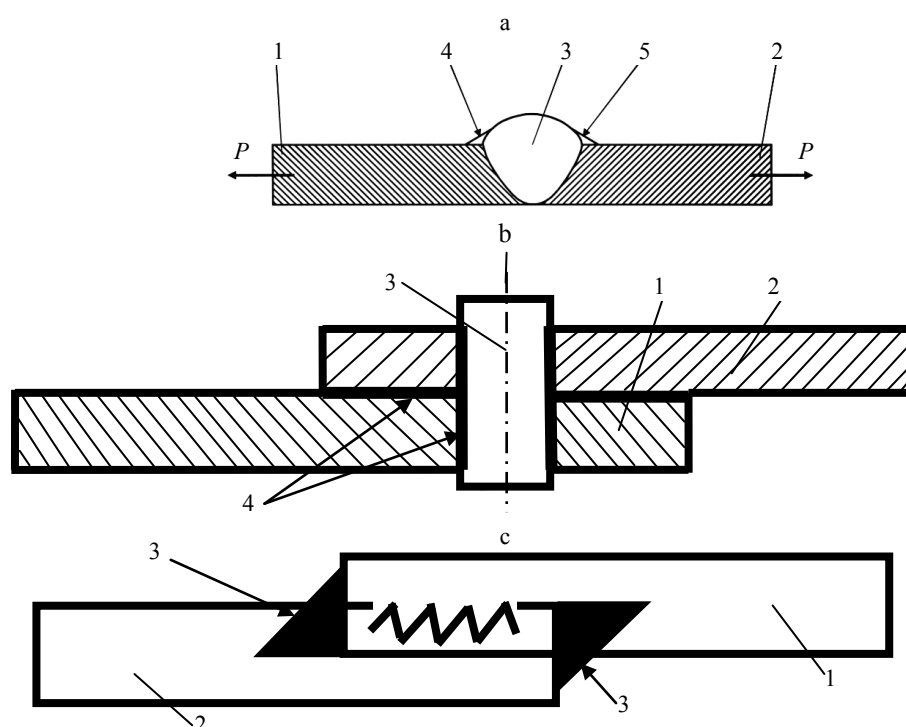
Схемы гибридных соединений: а – стыковое паяно-сварное: 1, 2 – соединяемые детали; 3 – сварной шов; 4, 5 – напайки; б – нахлесточное паяно-механическое: 1, 2 – соединяемые детали; 3 – упрочняющий стержень; 4 – паяный шов; в – нахлесточное механико-сварное: 1, 2 – соединяемые детали; 3 – сварной шов
